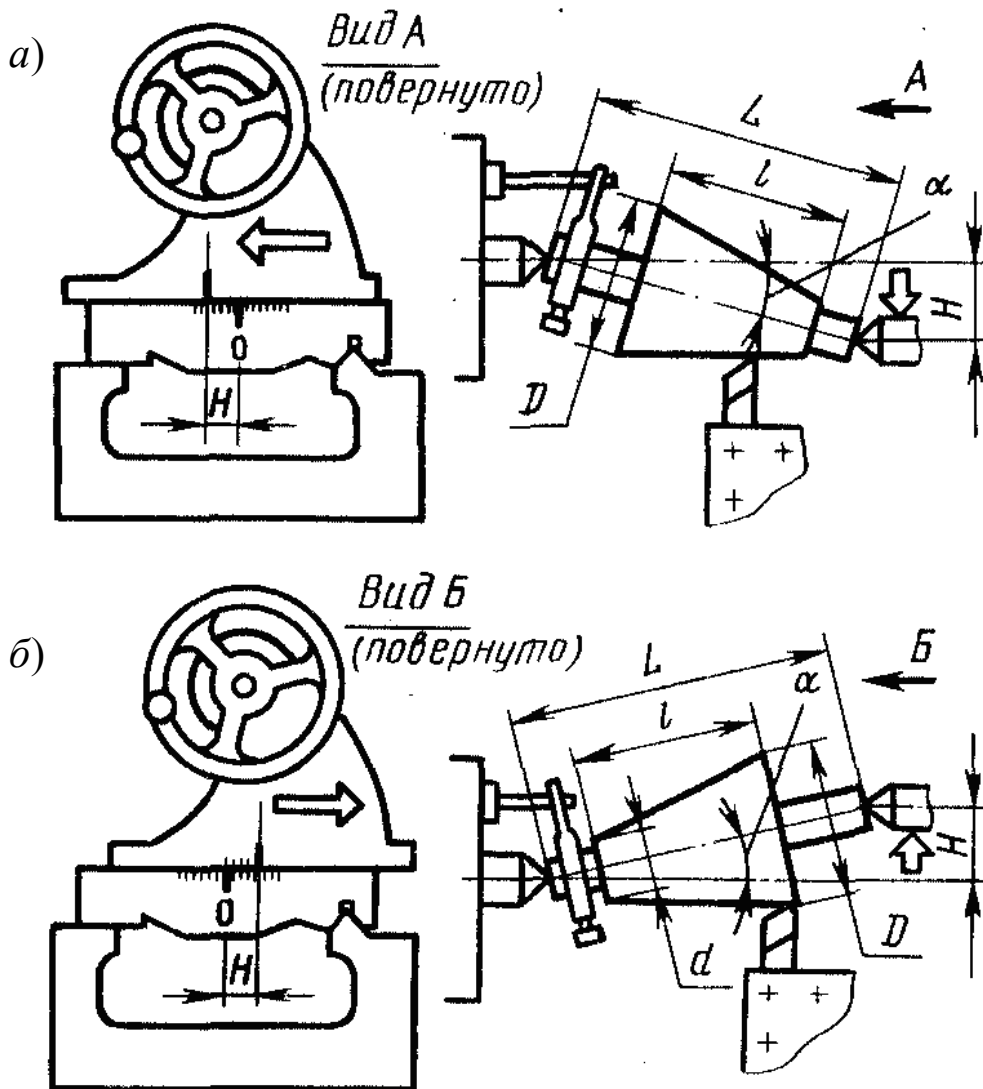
Обработка конических поверхностей способом смещения корпуса задней бабки
